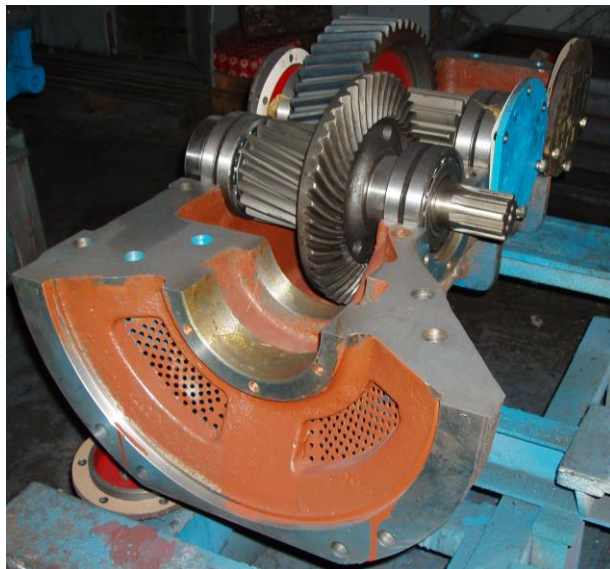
Вигляд у розрізі планетарного редуктора
